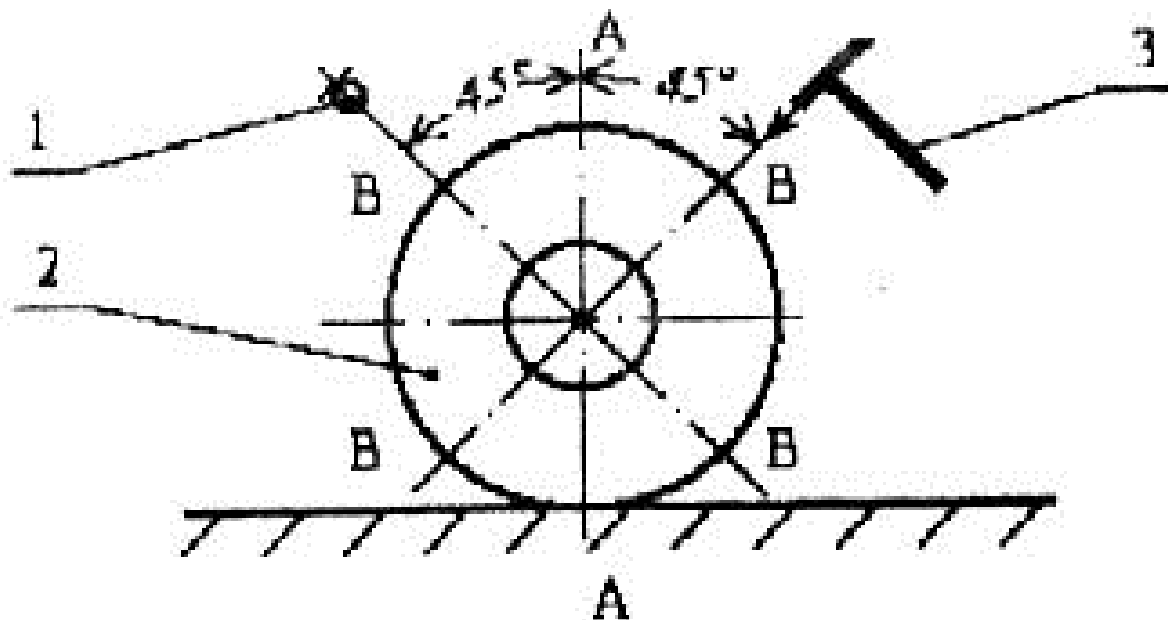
Схема расположения круга при проведении измерений (1 – микрофон; 2 – измеряемый круг; 3 – молоток; AA – диаметр, проходящий через опору; BB – возможные зоны расположения ударника и микрофона)
